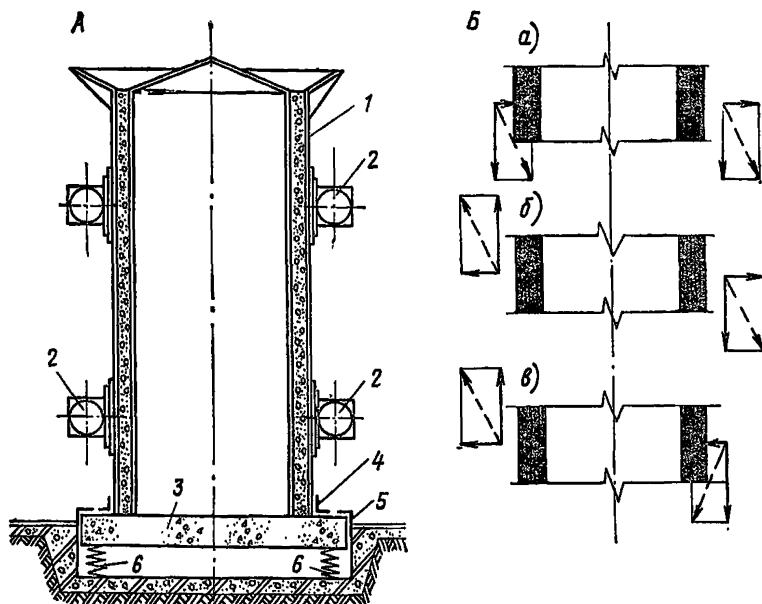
Форма для изготовления железобетонных труб на виброизолированном поддоне
